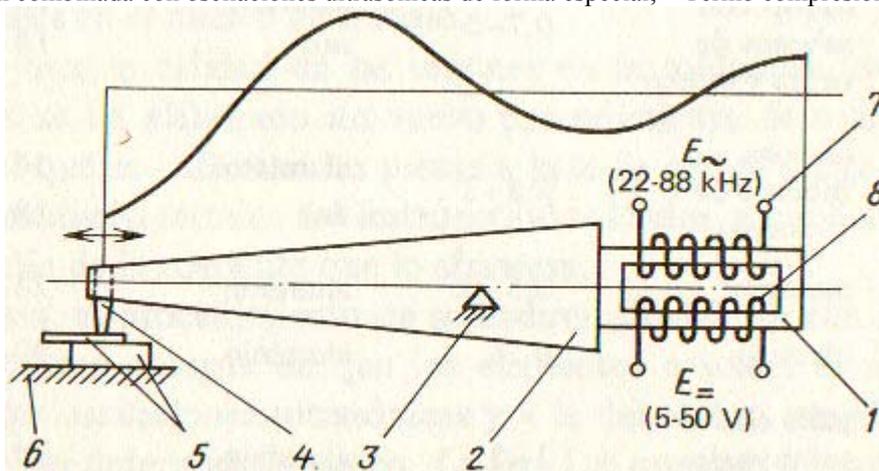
Soldadura Ultrasónica con oscilaciones longitudinales: 1- Transformador Magnetostrictivo; 2- guía ondas; 3- soporte y mecanismo para la creación de la fuerza y presión; 4- instrumento soldador: punta; 5- piezas a soldar; 6- soporte para la fijación de las piezas; 7- devanado de excitación; 8- devanado de imantación.
